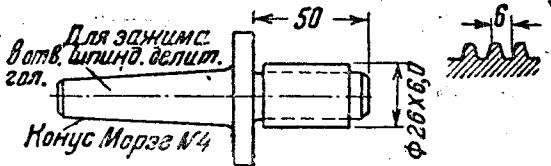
Схема фрезерования регулировочной гайки по новому технологическому процессу:
